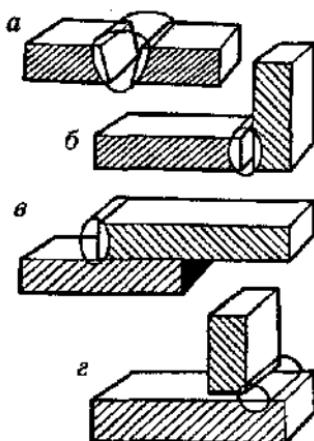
Сварные соединения: а — стыковое; б — угловое; в — нахлесточное; г — тавровое.
